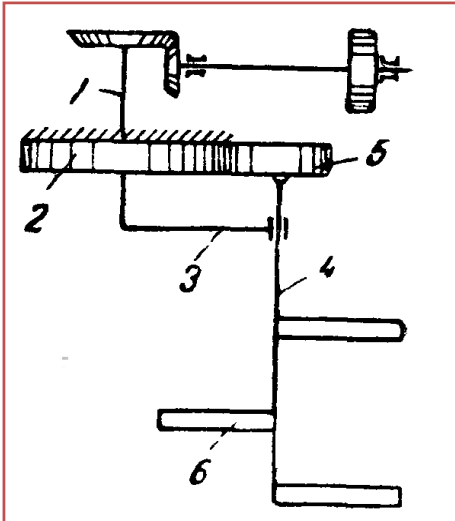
Планетарна мішалка: 1–вертикальний вал, 2–нерухоме зубчасте колесо, 3– водило, 4 – вал, 5 – зубчасте колесо, 6 - лопатки
